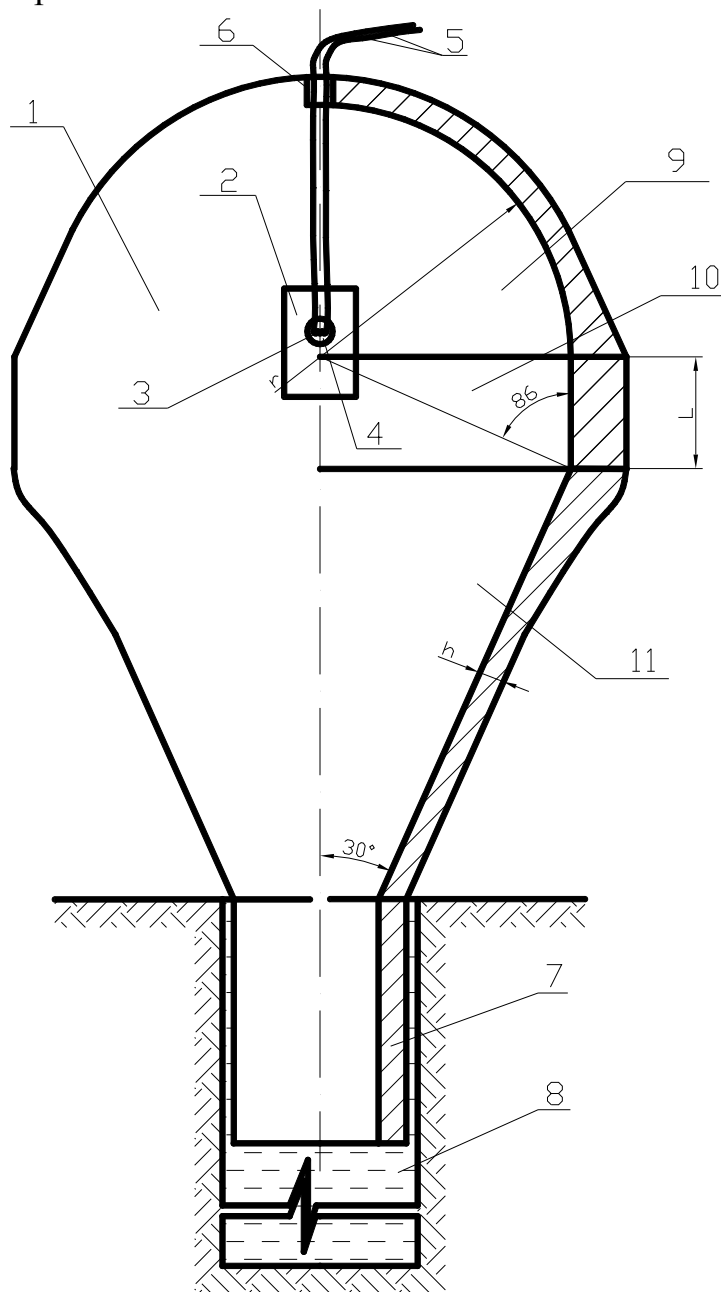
Загальний вигляд установки для блочного відділення каменю
